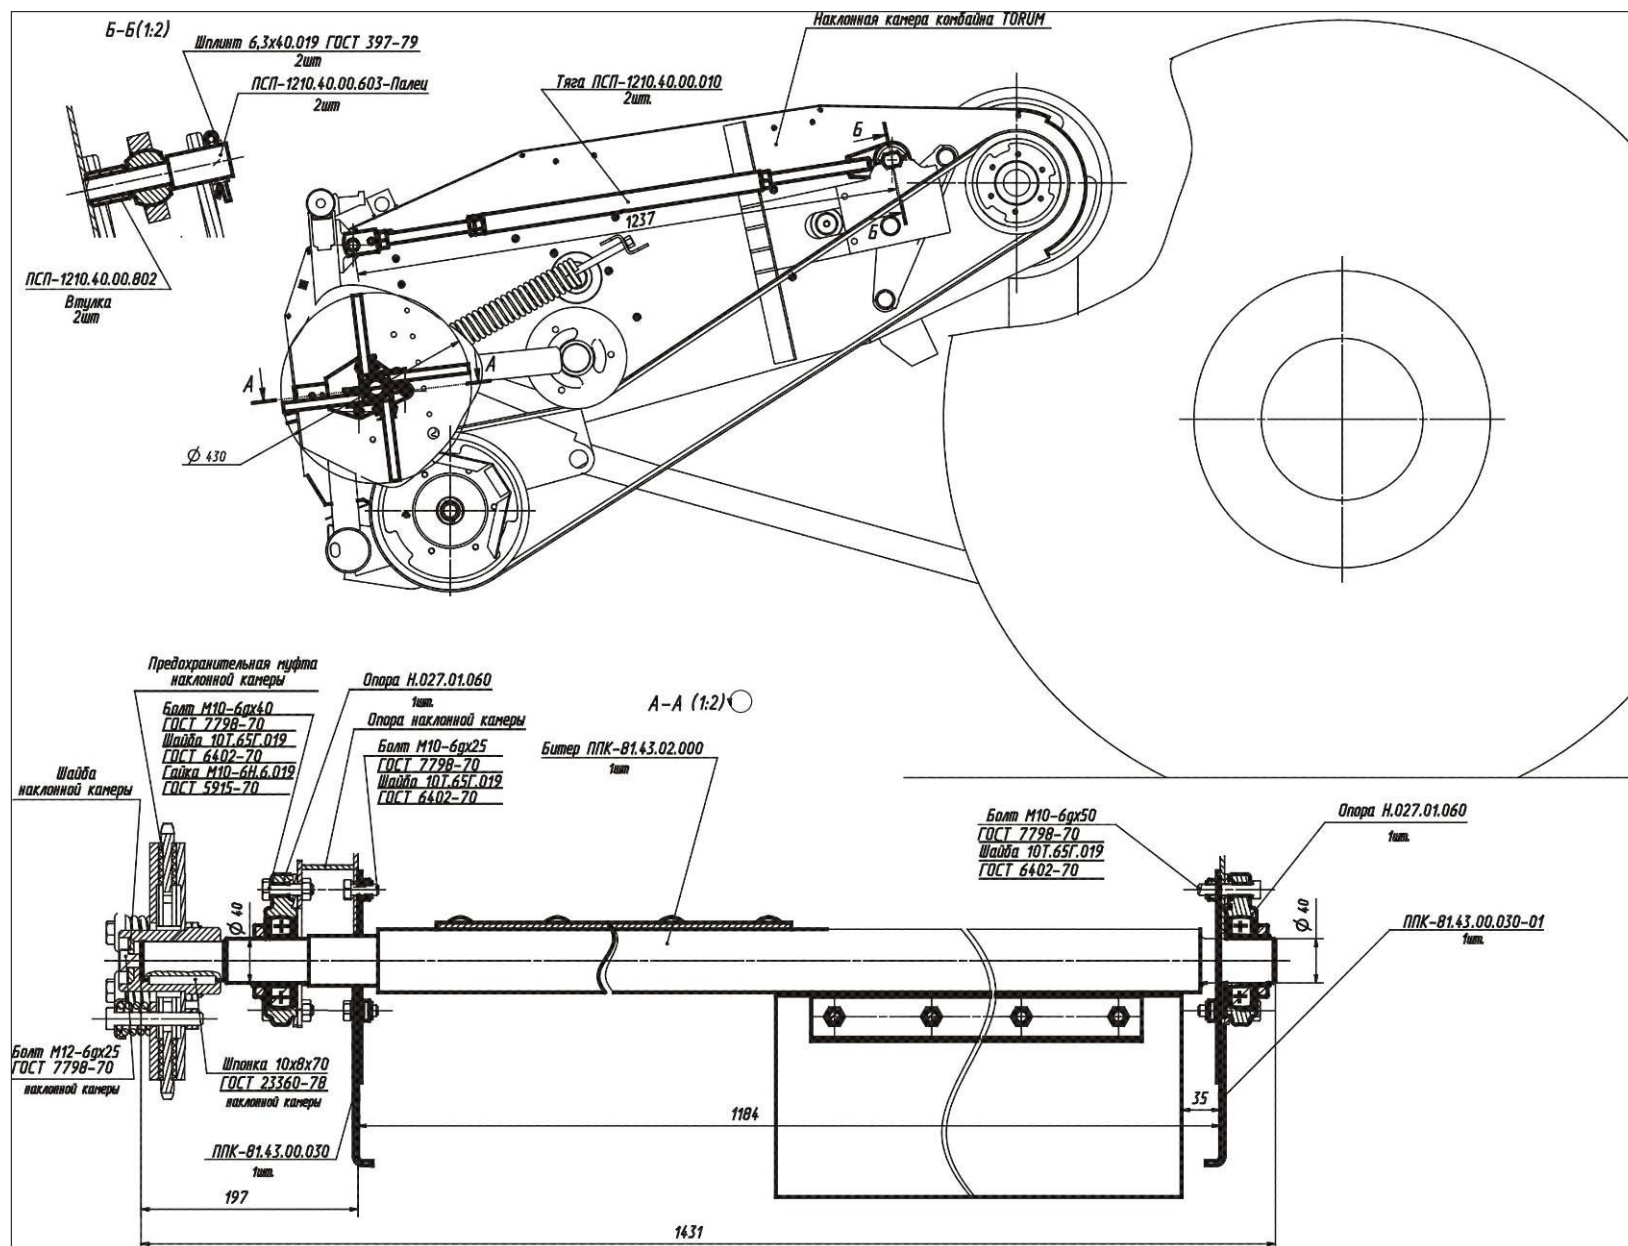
Установка битера приспособления ППК-870-11
